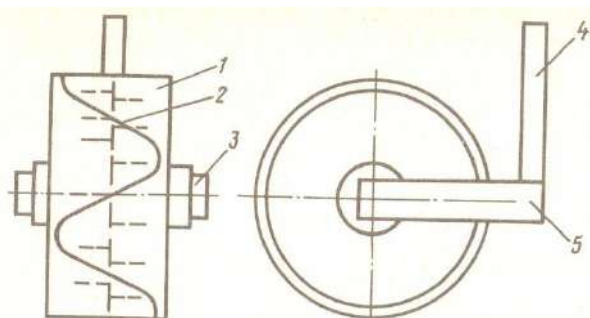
Каток-бороздодел: 1-цилиндр; 2-выступ; 3-ось; 4-стойка; 5-вилка.
